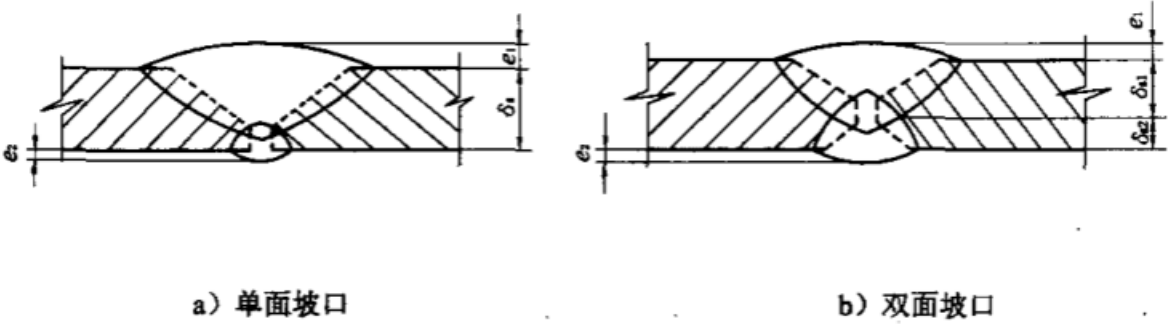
A、B 类焊接接头焊缝余高测量示意
